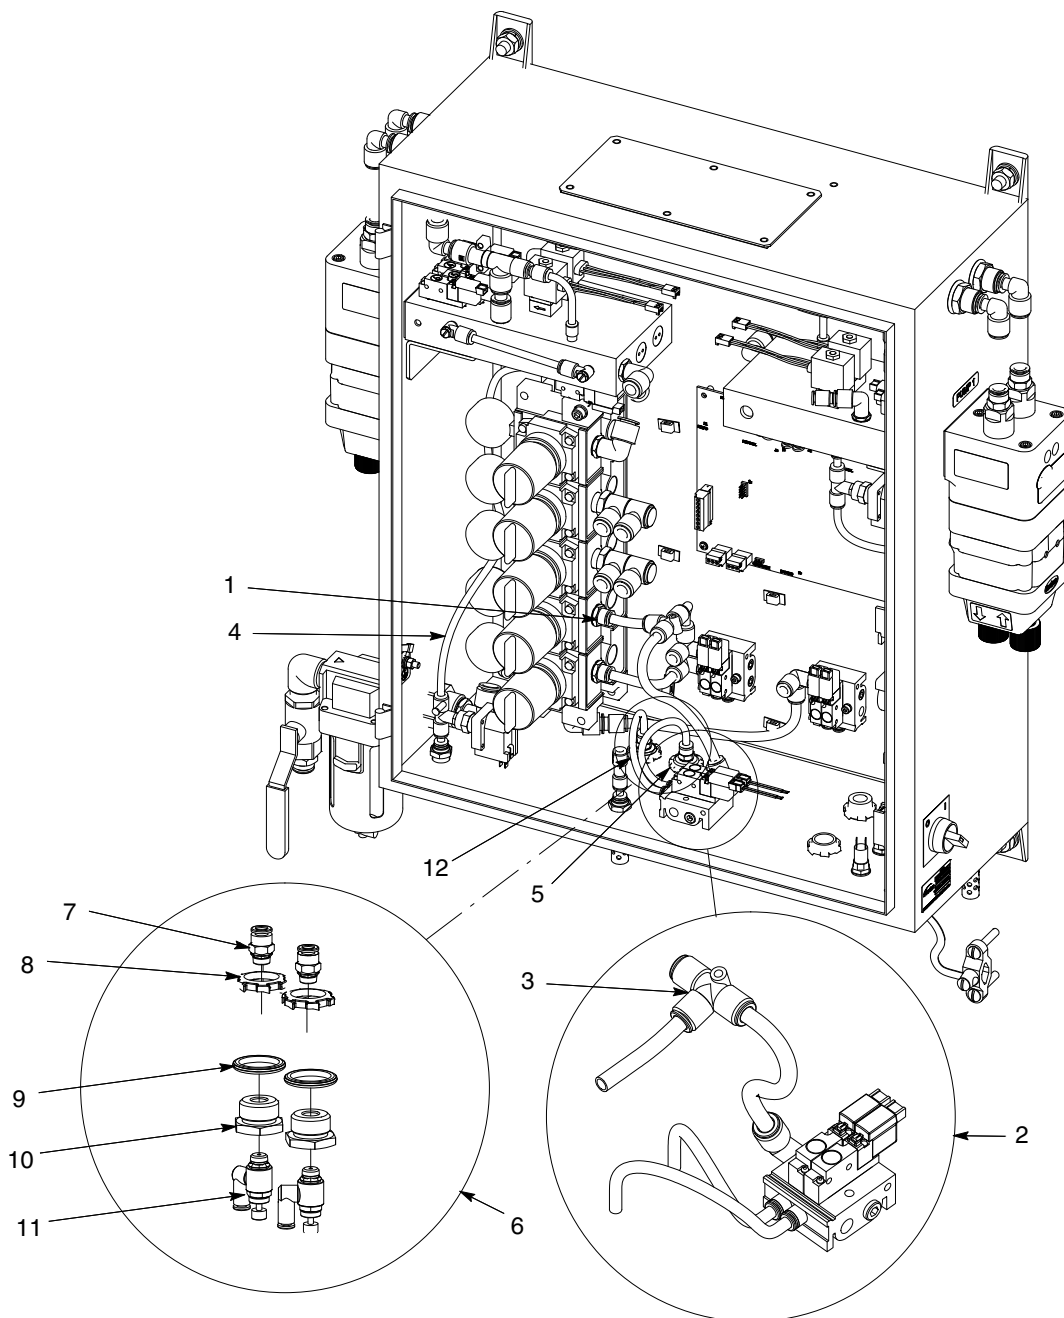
Komponenten des Pumpenschaltschrank (Abb.: Version mit zwei Pistolen)
